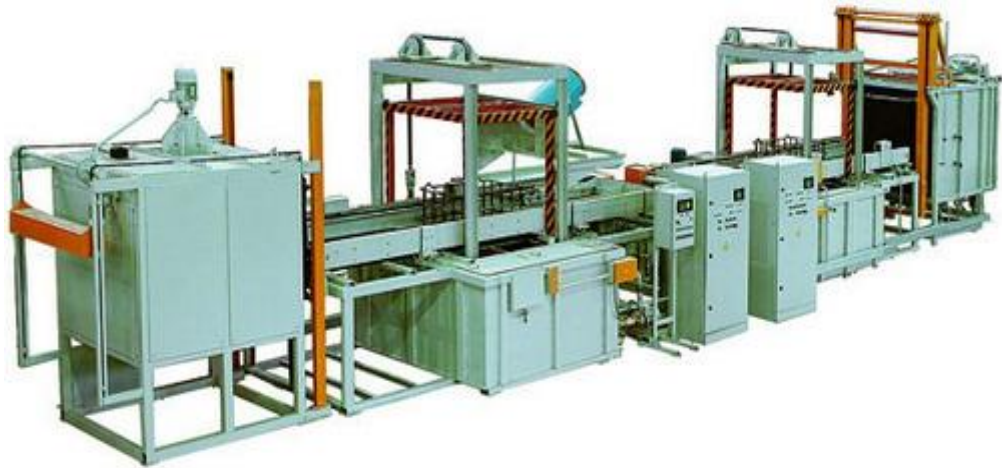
Камерный механизированный агрегат СНЗА 6.12.5/7
